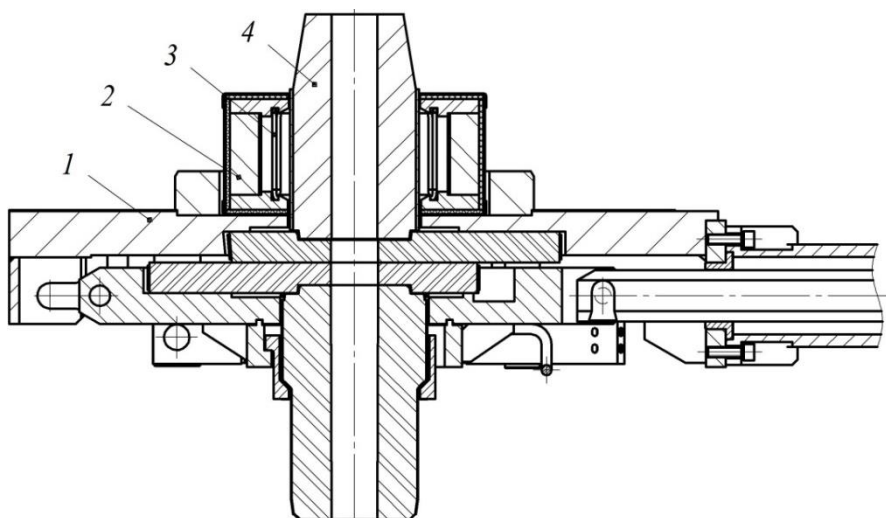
Схема усовершенствованной конструкции шиберного затвора литейного ковша
